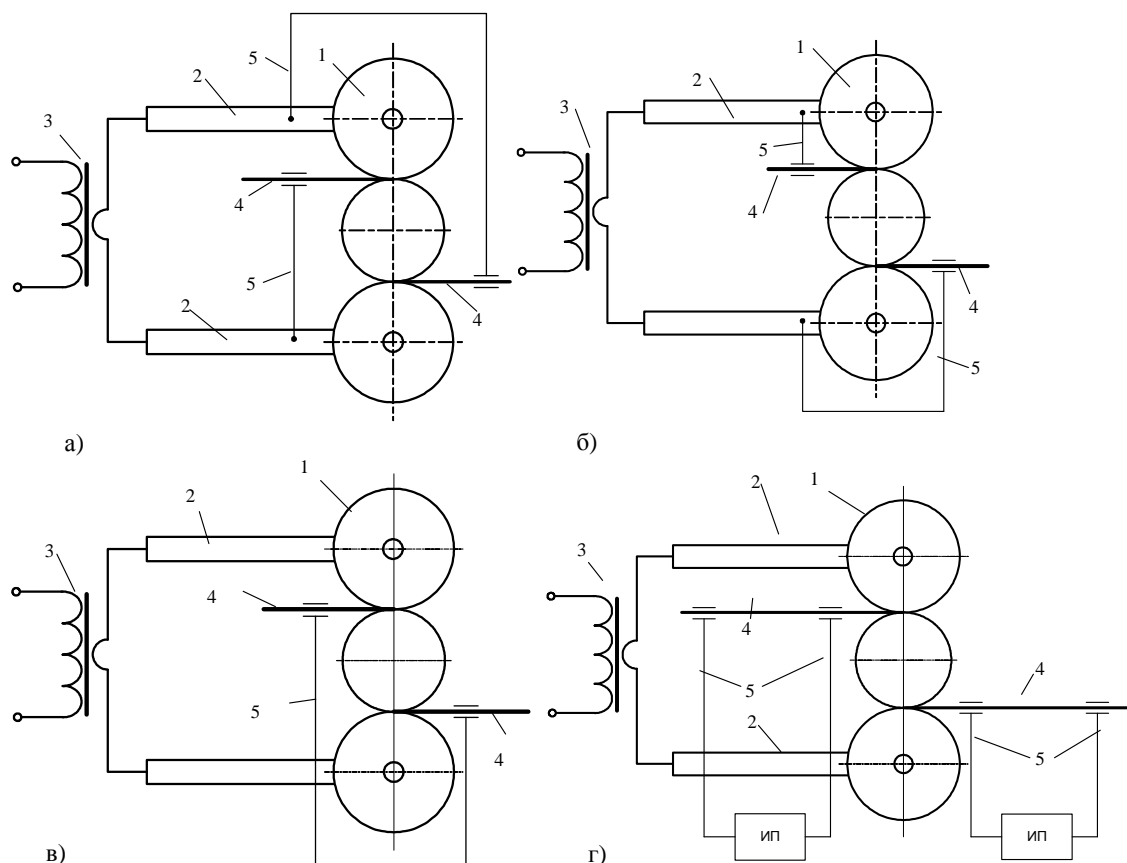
Технологические схемы предварительного нагрева привариваемой проволоки: а-в) с включением в сварочную цепь установки для наварки; г) от отдельных источников питания ИП. (1 – роликовый электрод; 2 – клещевина; 3 – сварочный трансформатор, 4 – привариваемая проволока; 5 – токоподводы к проволоке)
